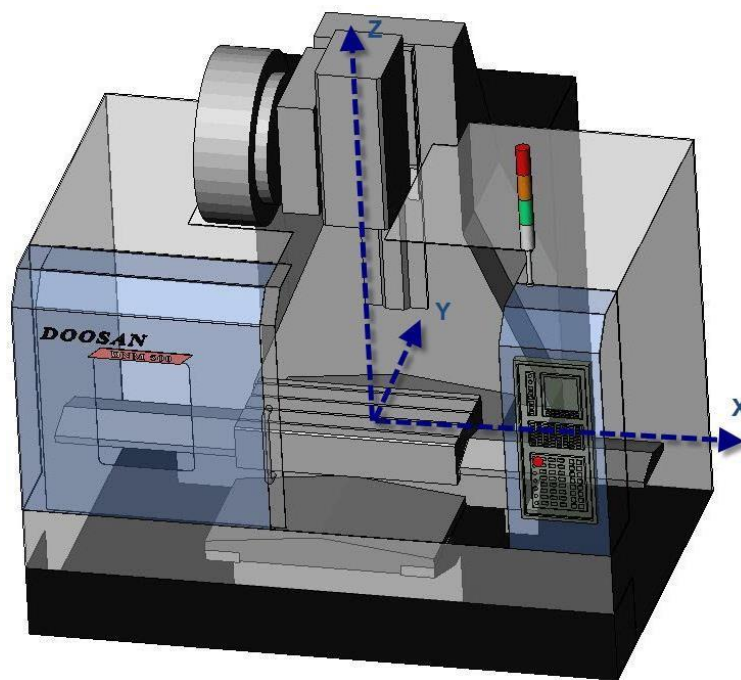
Общий вид системы координат фрезерного станка с ЧПУ
